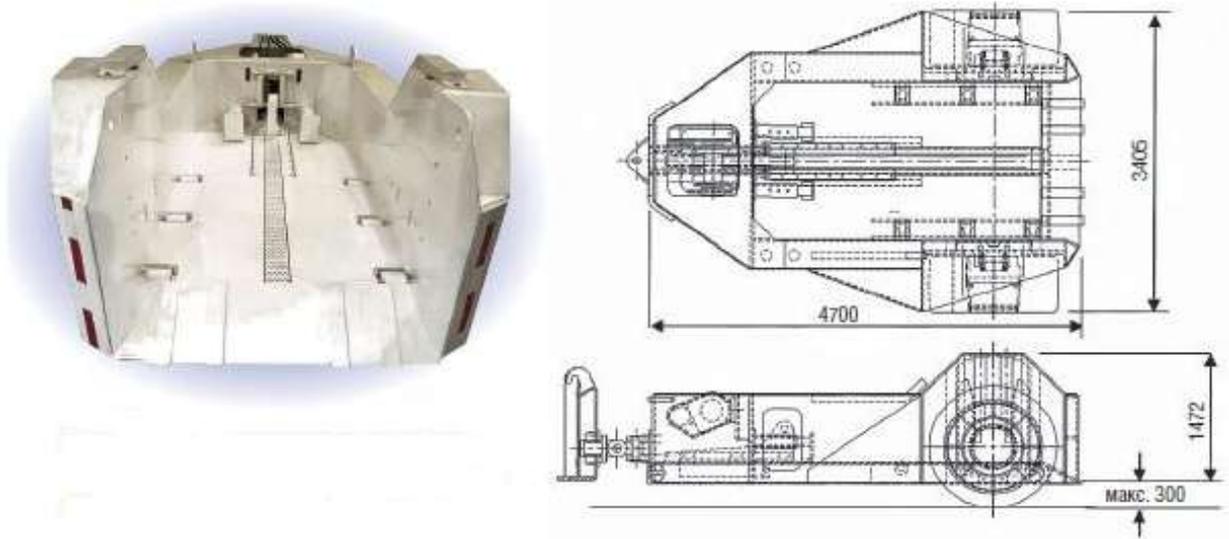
Общий вид и чертеж трейлера СНТ-50
